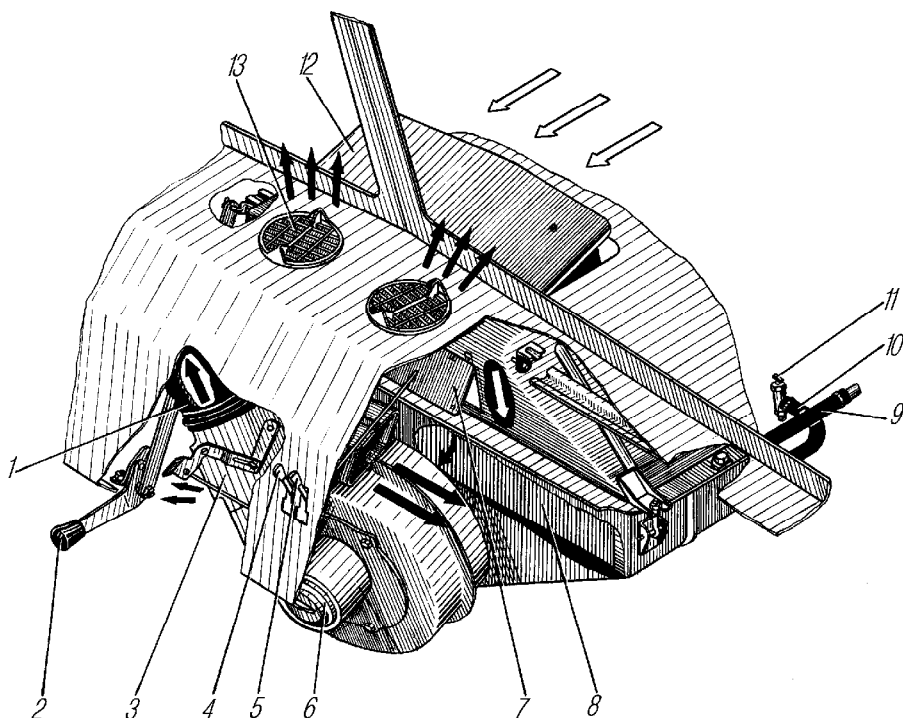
Схема действия отопителя кабины и обдува ветрового стекла: 1- патрубок подачи теплого воздуха для обдува ветровых стекол; 2- рукоятка привода наружного люка; 3- распределитель воздухообогрева; 4- рычаг привода заслонок распределителя воздухообогрева; 5- рычаг привода внутреннего люка; 6- электродвигатель с вентилятором в сборе; 7- крышка люка внутреннего; 8- радиатор отопителя; 9- труба водоотводящая из радиатора отопления; 10- труба водоподводящая; 11- краник; 12- крышка люка наружного; 13- дефлектор
